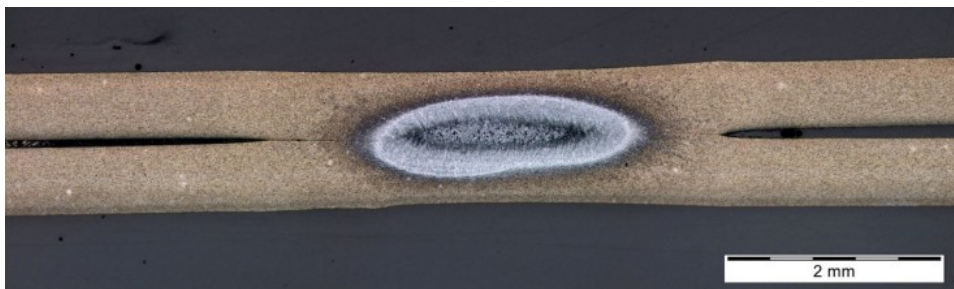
Section d'un échantillon soudé - plaquettes nettoyées au laser (EN AW-2024-T3)
